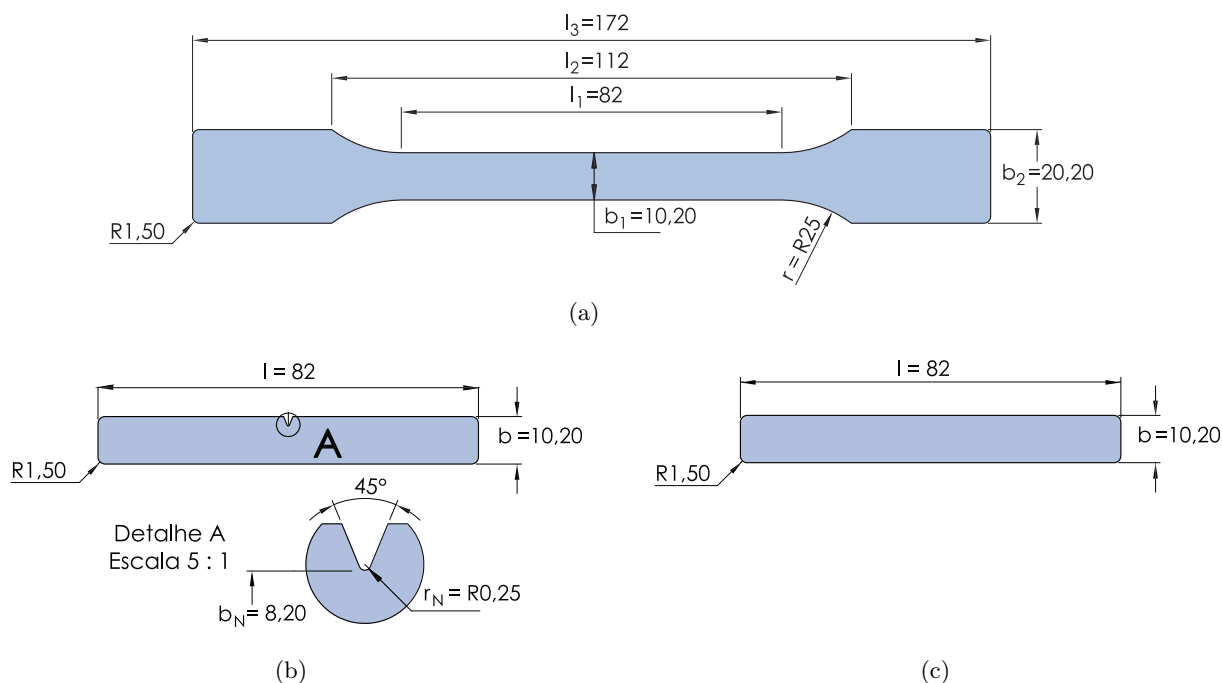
Dimensão da zona moldante do provete de: (a) tração, (b) impacto com entalhe e (c) impacto sem entalhe ou flexão.
